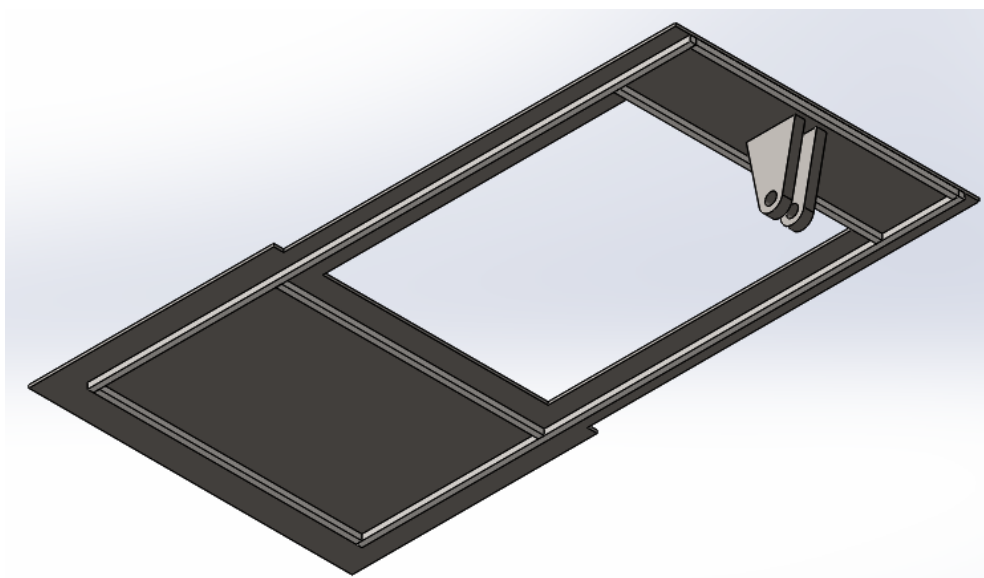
Vista de baixo do alçapão com a forquilha e a estrutura de reforço
